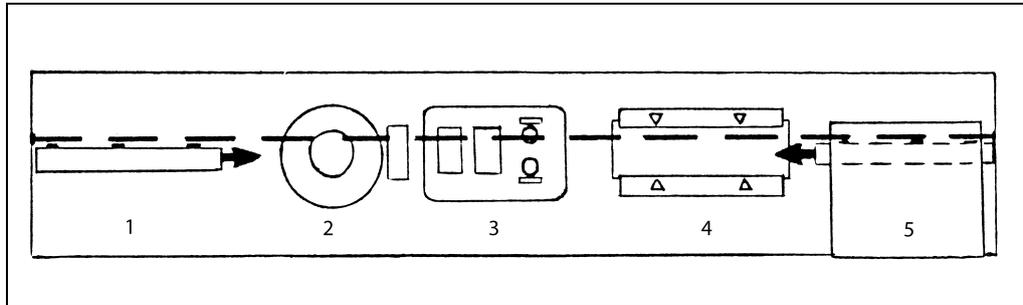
Schlittenmaschine: 1 Handeinlage in Klammer, 2 Rückenbearbeitung, 3 Klebstoffauftrag, 4 Umschlaganpressen, 5 Rutschauslage
